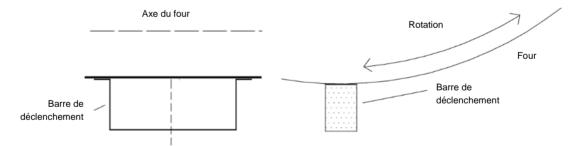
Soudage de la barre de déclenchement sur le four
